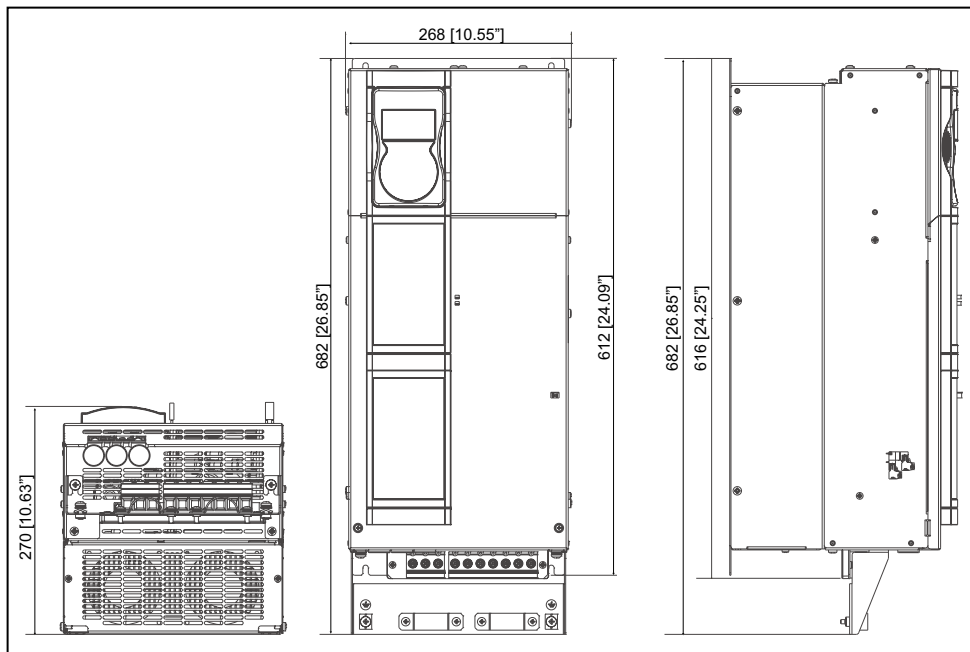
Размеры для типоразмера 4 (ADV200-...-4)
